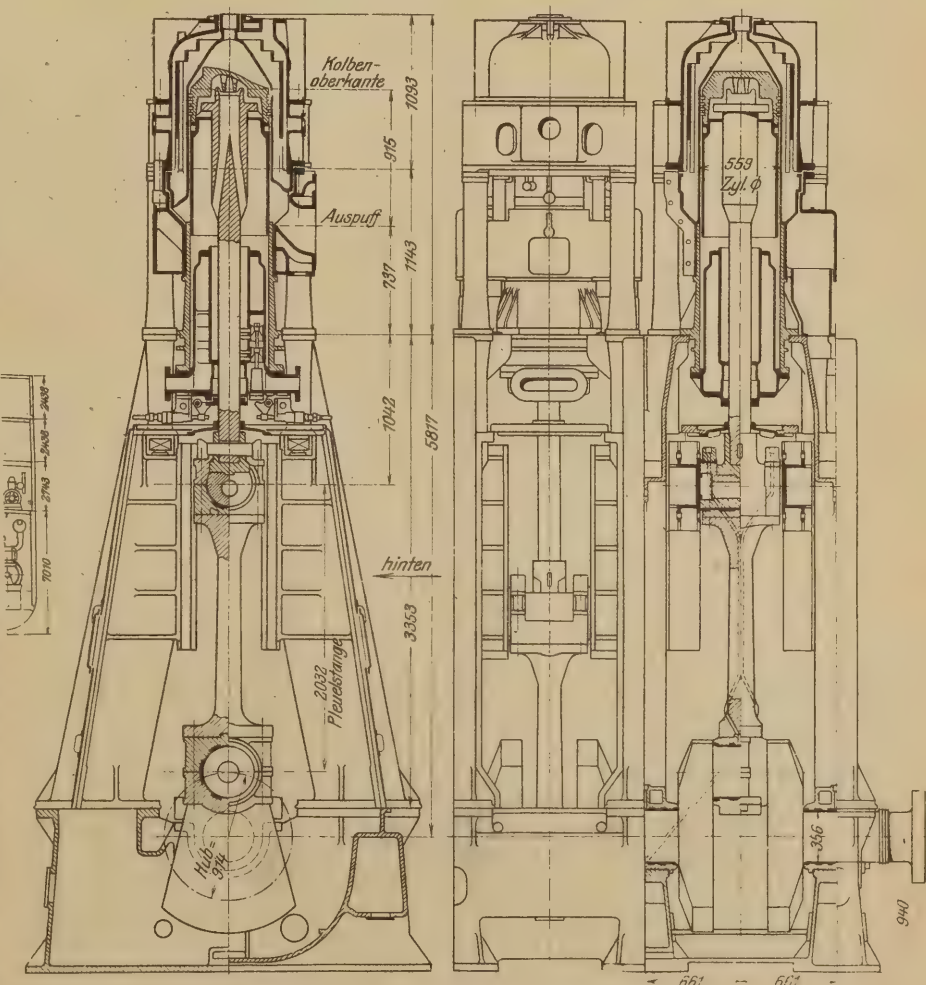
und 2. Scott-Still-Schiffsdieselmachine.
